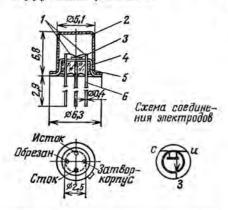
Полевой транзистор КП103 в металлостеклянном корпусс: 1— волотые проволоки; 2— корпус; 3— кристалл; 4— ножка; 5— изолятор (стекло) 6— вывод.
